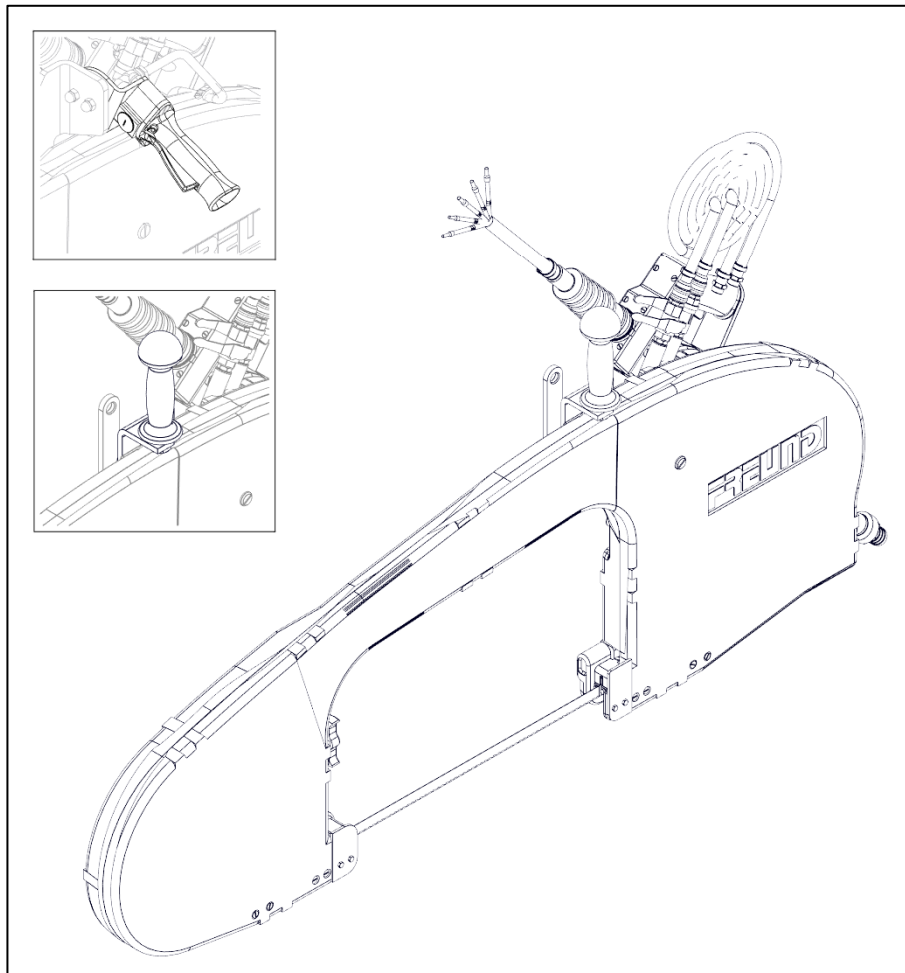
Ansicht Standardmaschine SB50-08 mit Detail Handgriff
